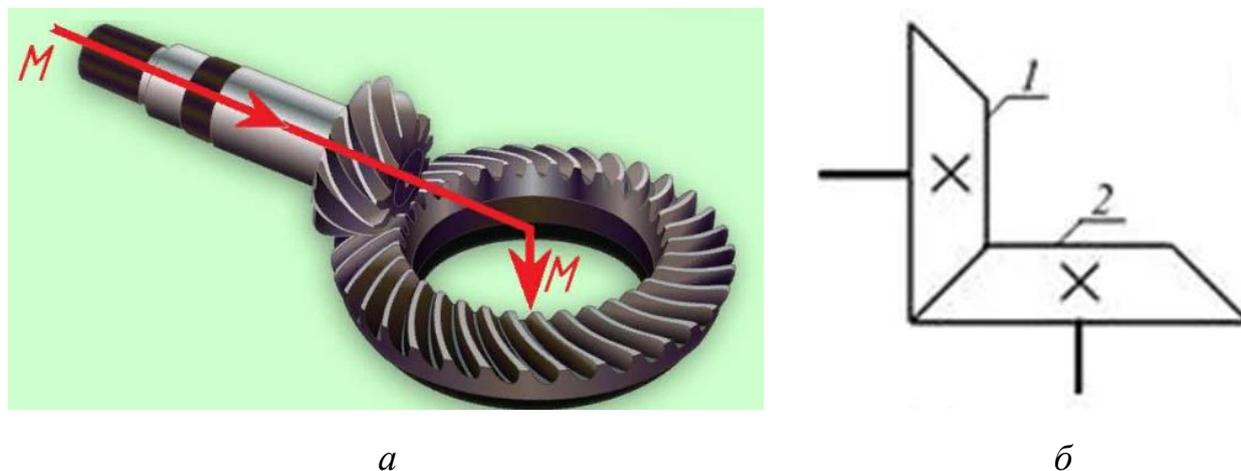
Коническая зубчатая передача: *а* – направление передачи крутящего момента; *б* – изображение на кинематической схеме
